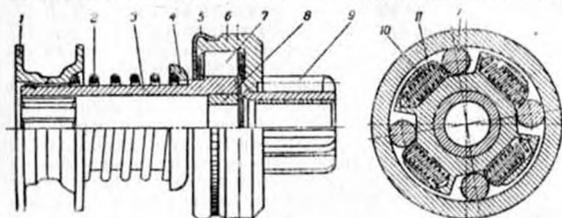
Механизм зацепления шестерни стартера с венцом маховика:
